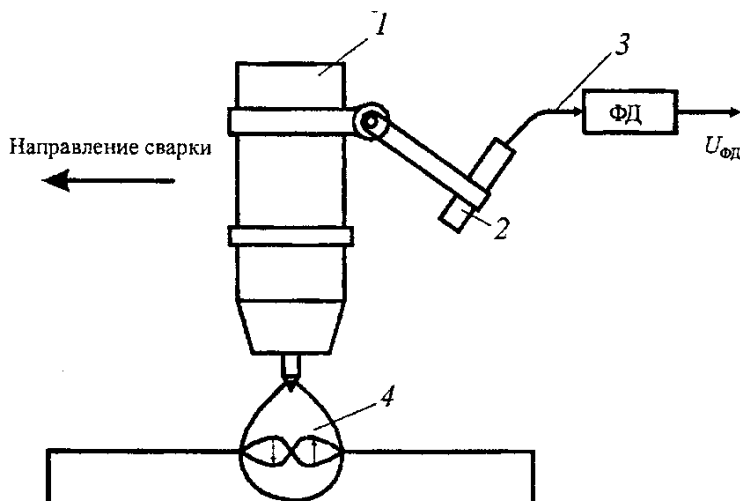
Схема установки оптического датчика на сварочной горелке: 1 – сварочная горелка; 2 – объектив; 3 – оптическое волокно; 4 – поверхность сварочной ванны [Installation scheme of the optical sensor on the welding torch: 1 – welding torch; 2 – lens; 3 – optical fiber; 4 – surface of the welding pool]
